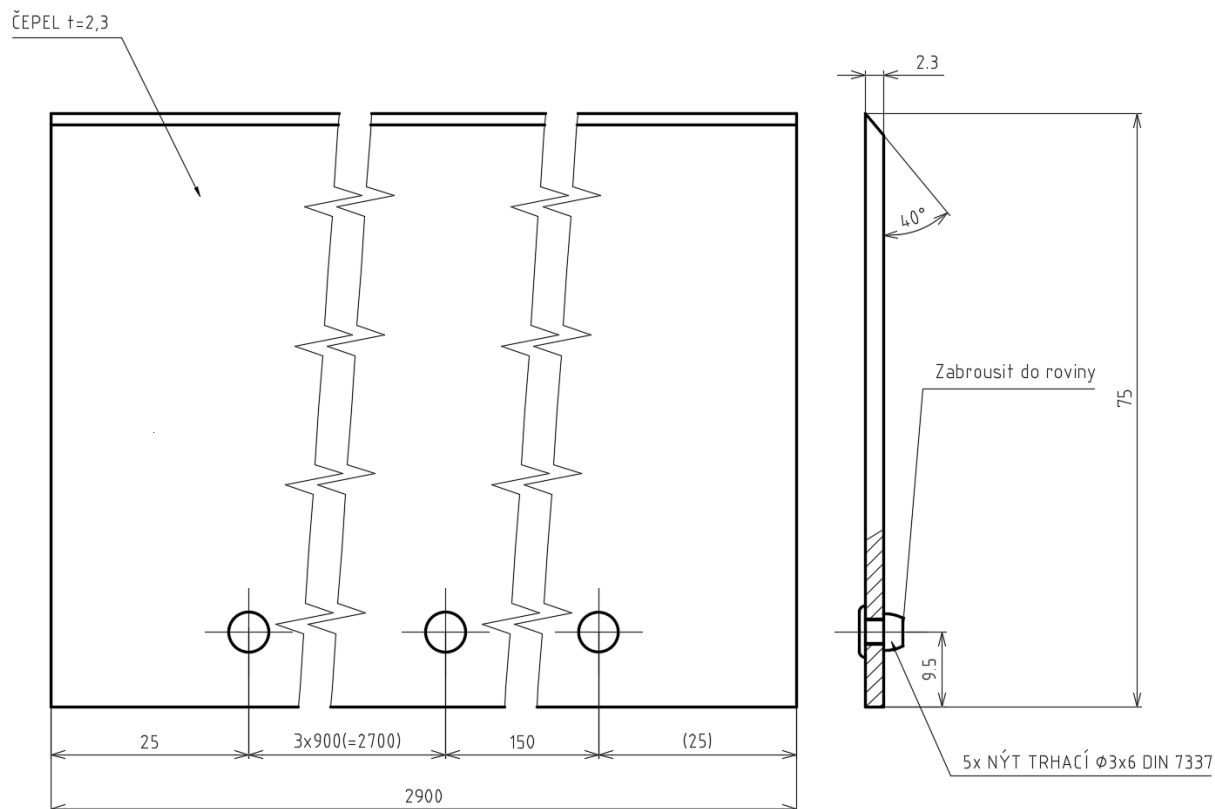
Konstrukční řešení držáku čepele – typ K35A
